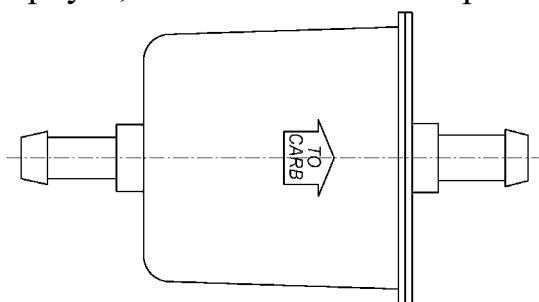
Фильтр тонкой очистки топлива неразборной конструкции
